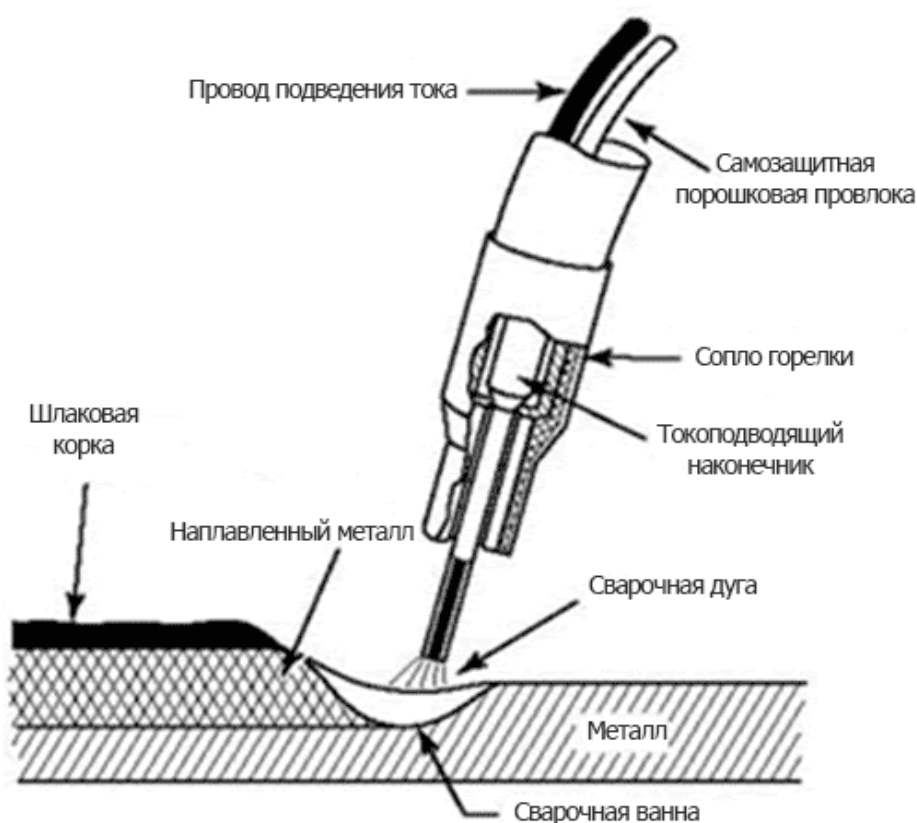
Схема выполнения сварки порошковой самозащитной проволокой
